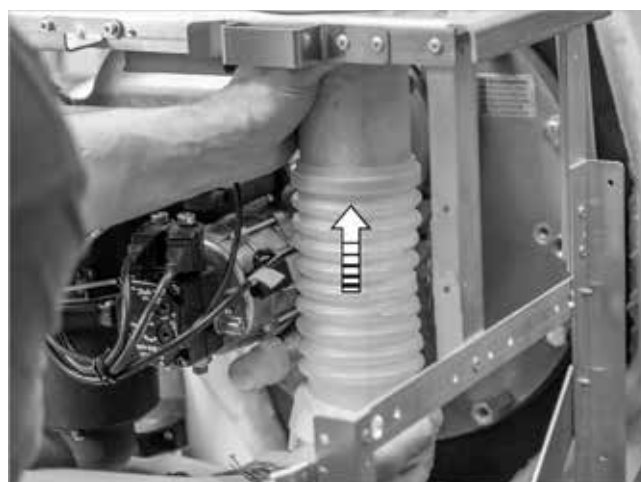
Montaggio raccordo per lo scarico dei fumi
